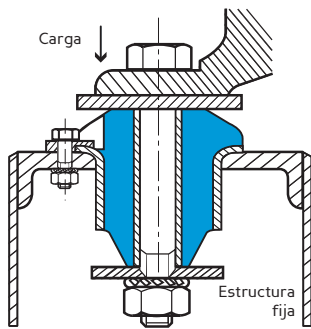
Montaje entre pie de la máquina y chasis metálico.
